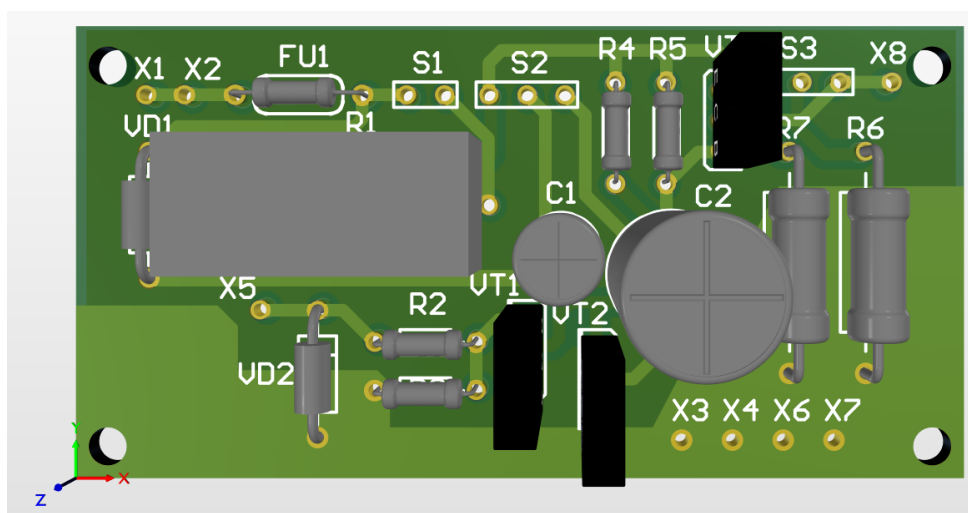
Трехмерный вид платы (верхний слой)
